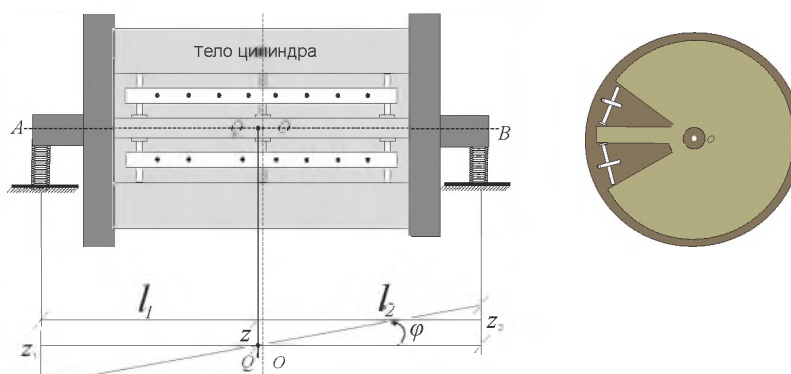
Стандартный формный цилиндр: вид спереди и с торца.
